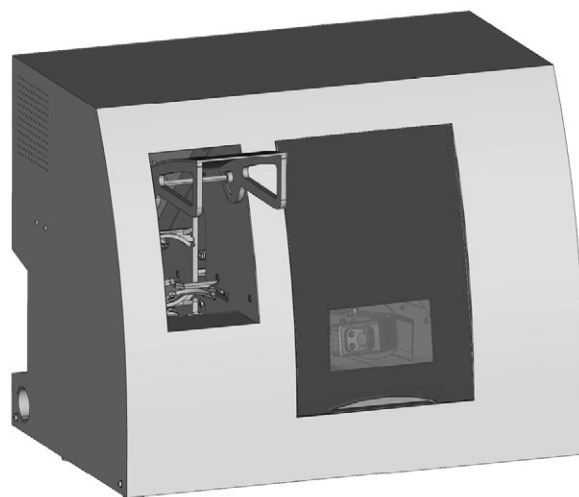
PORTE DU MAGASIN DE PIÈCES BRUTES
